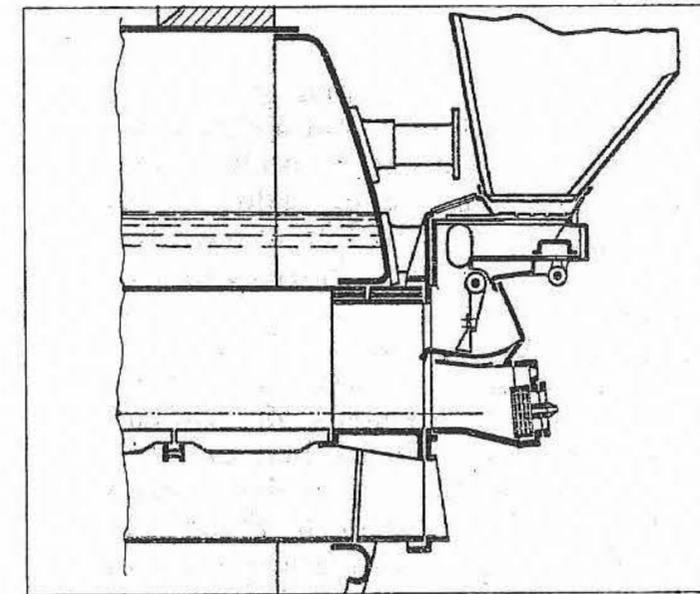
/6: Beispiel für eine Innenfeuerung bei einer Halblokomobile mit Flammrohrkessel mit selbsttätiger Zufuhr der Kohle durch „Schleuderfeuerung“ (um 1910)
